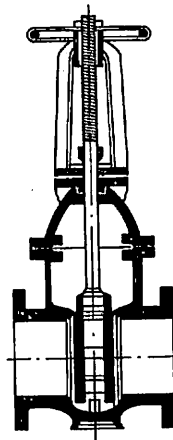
Parallelovalschieber mit Bockaufsatz, Spindel steigend
